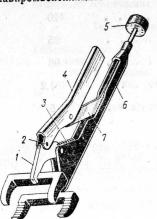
1 — корпус; 2 — винт регулировочный; 3 — ручка; 4 — пружина; 5 — губка подвижная
